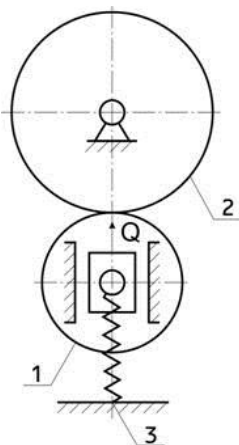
Фрикционный механизм с цилиндрическими катками
